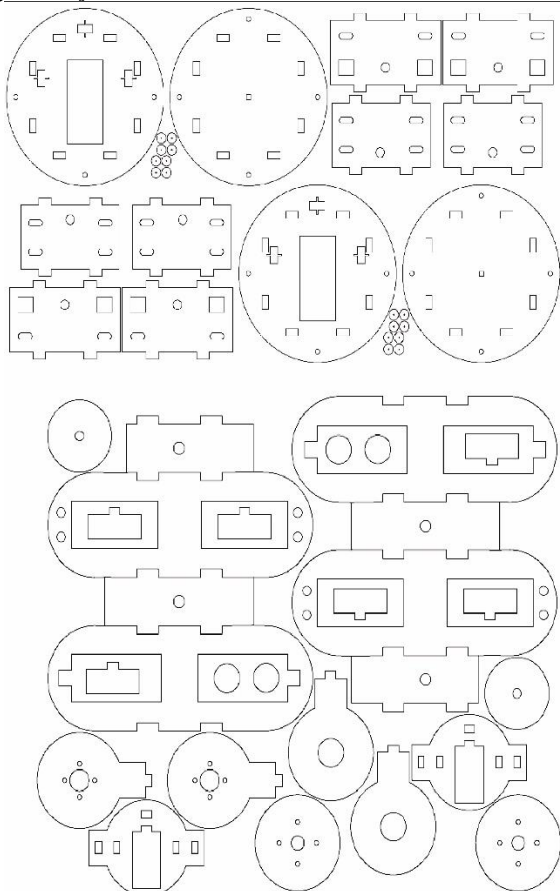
Piezas para manufactura de Cintra mediante corte laser mediante el CAM.
